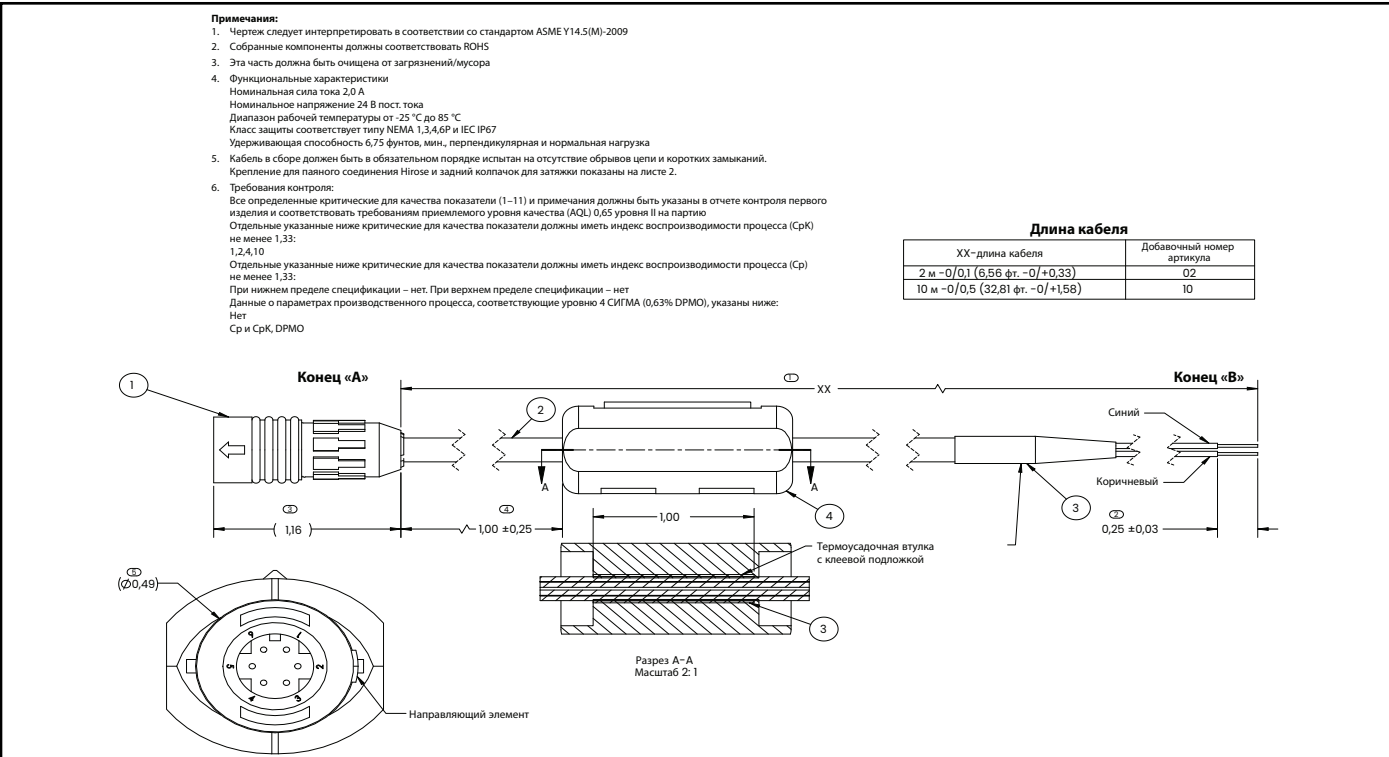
Кабель, стандартный (№ чертежа 704-1317, лист 1 из 2)
